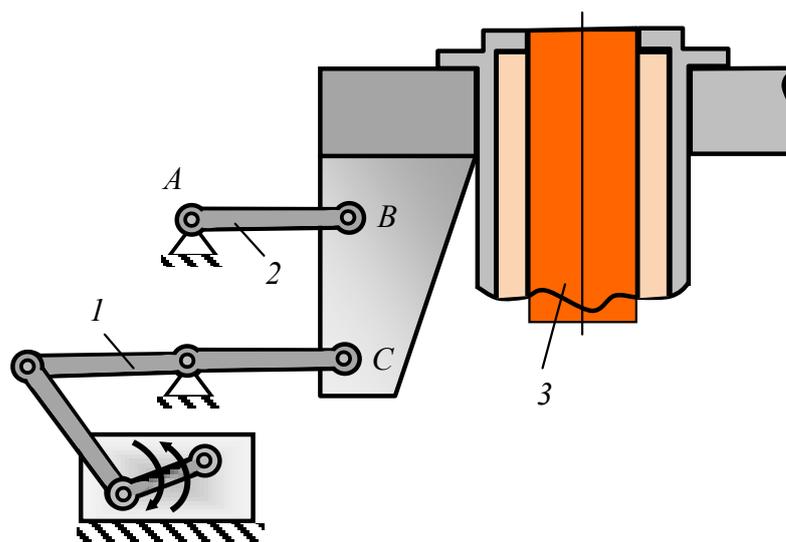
Кинематическая схема механизма качения кристаллизатора
